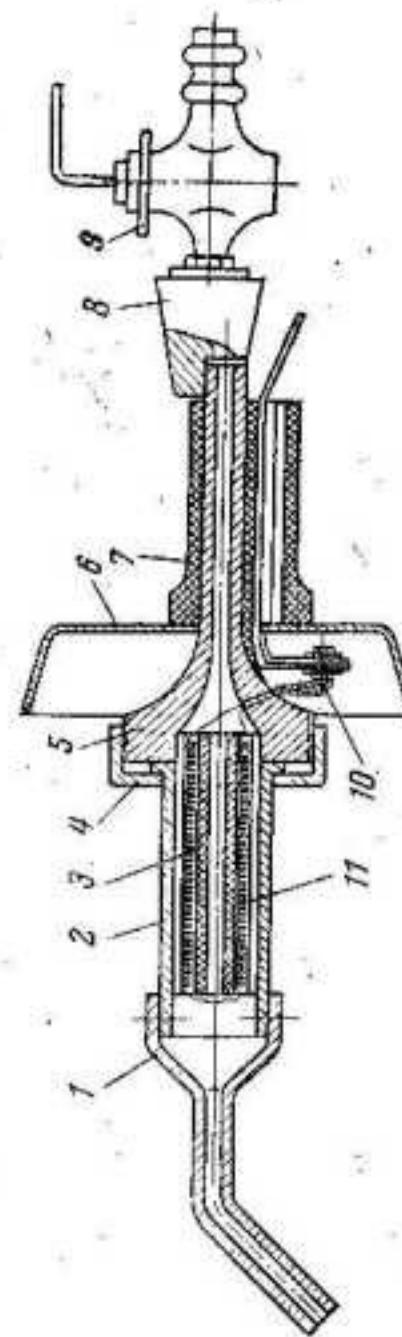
Воздушная электрическая горелка для сварки винилластовых труб.
